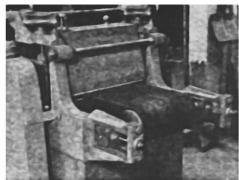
,1. Modo de estar soportado el tambor tensor de la máquina desbarbadora (figs. 10,1 y 2)
